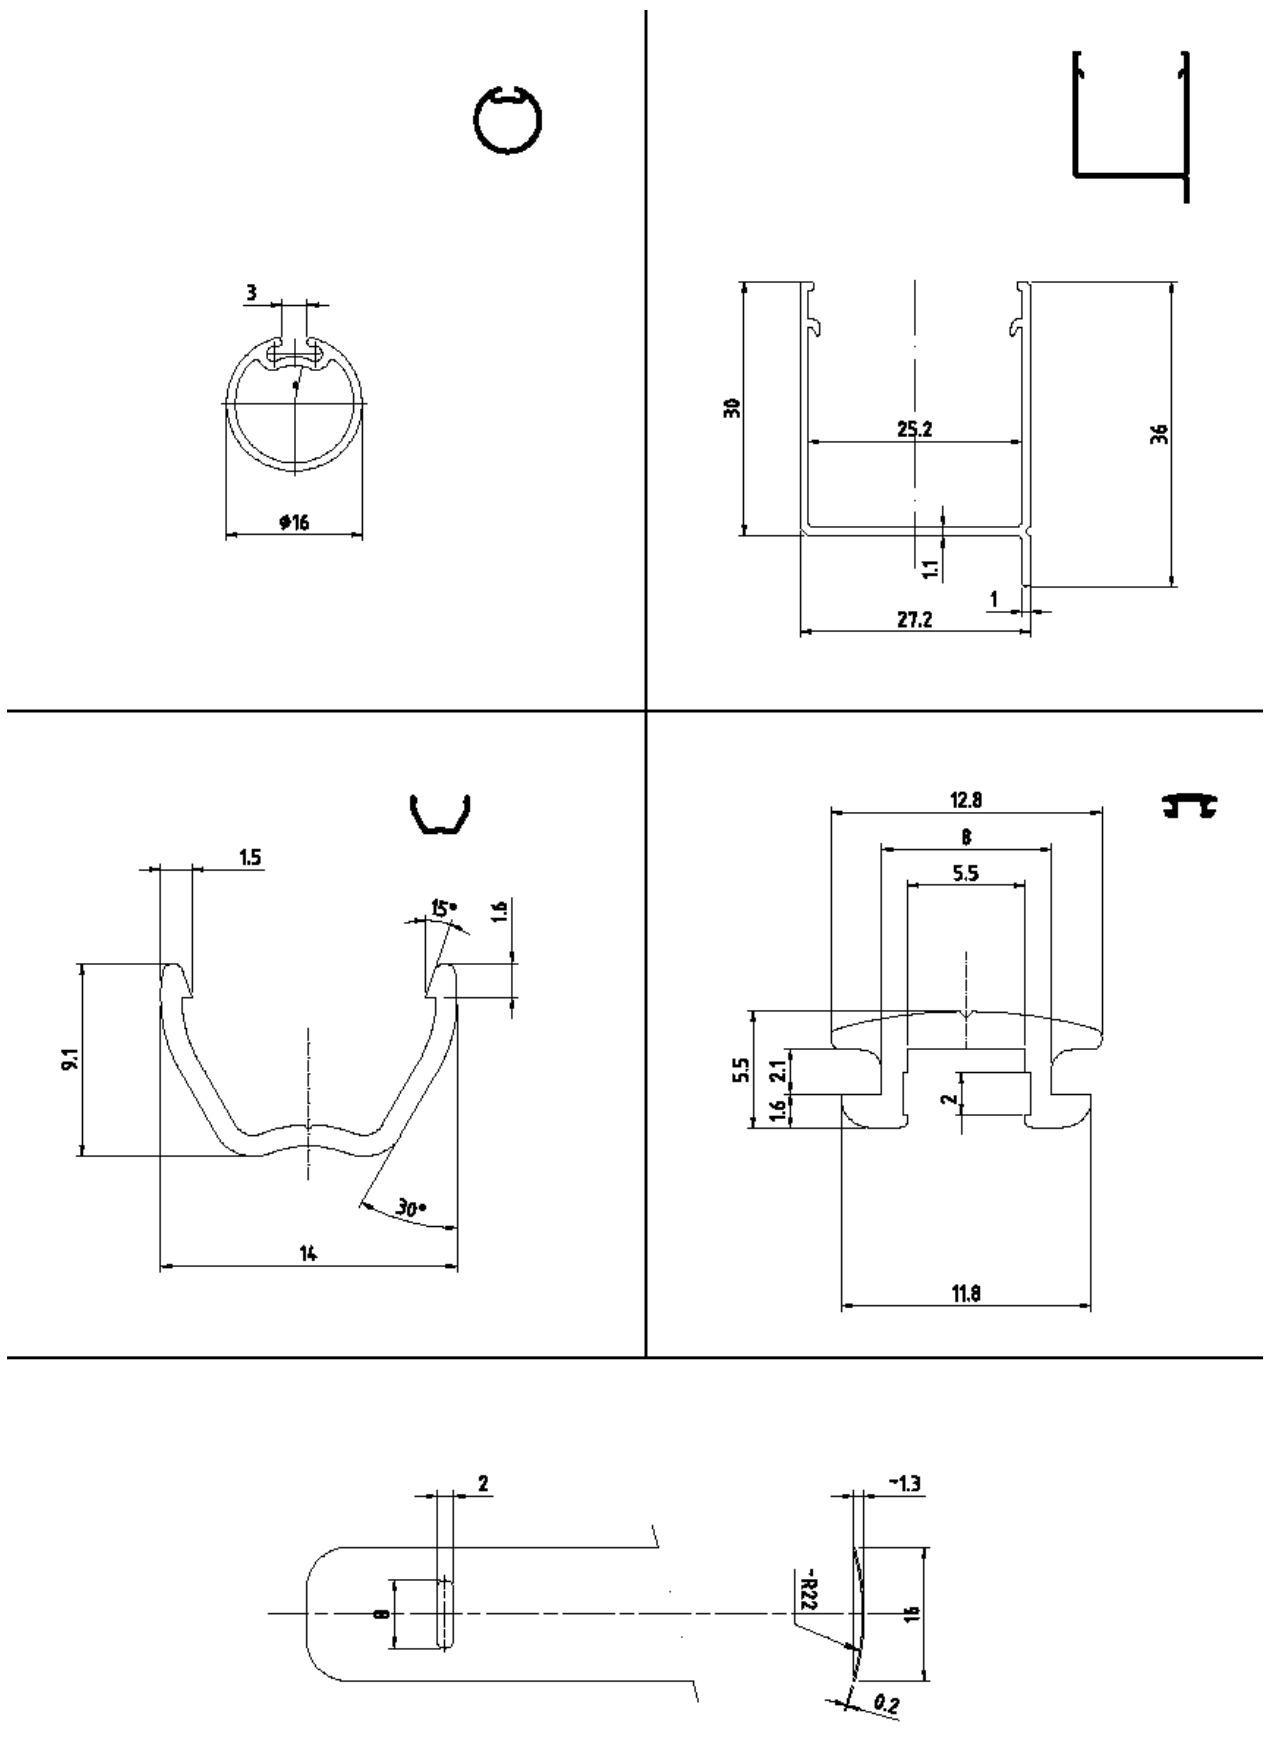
Tube aluminium d'entraînement - Boîtier haut - Éléments constituant la barre de charge lamelle store et usinage
